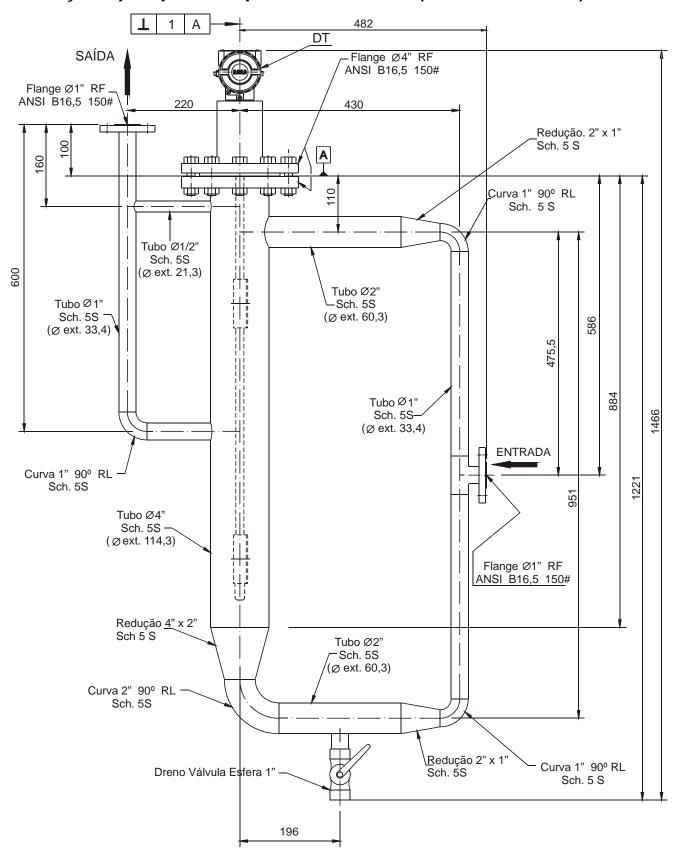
Tipos de Instalação para o DT302 (A)
